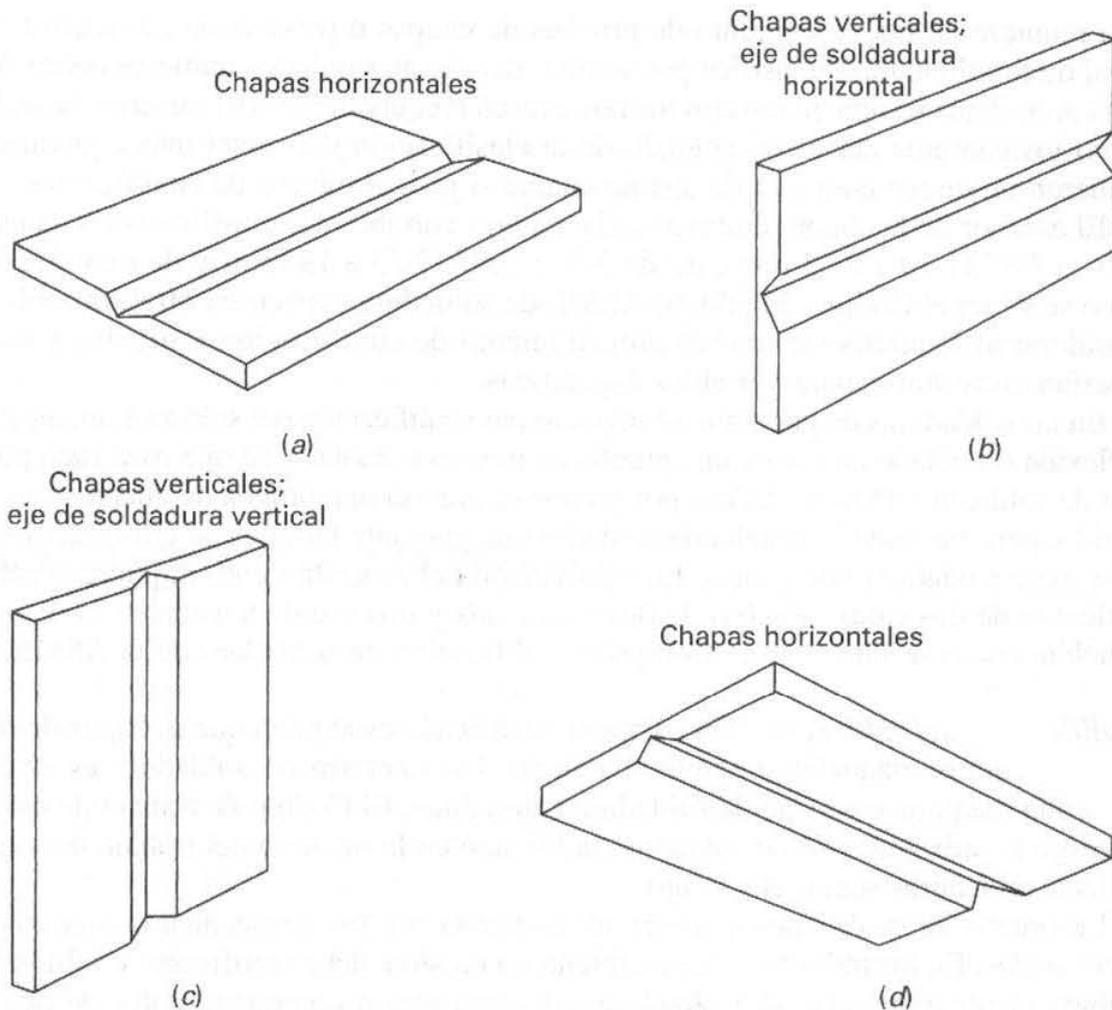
Código de posiciones de soldar para soldaduras de garganta utilizadas para cualificar operadores. Posiciones de las pruebas: (a) 1G; (b) 2G; (c) 3G; (d) 4G.
